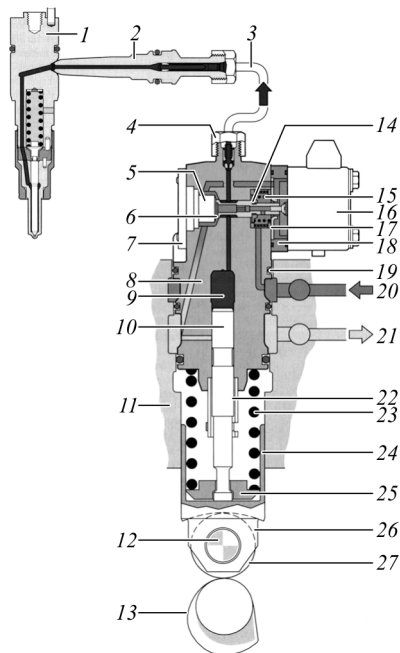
Схема системы насос – форсунка – трубопровод: 1 – форсунка; 2 – штуцер форсунки; 3 – трубопровод высокого давления; 4 – накидная гайка; 5 – упор; 6 – игла электромагнитного клапана; 7 – пластина; 8 – корпус насоса; 9 – полость высокого давления; 10 – плунжер; 11 – блок двигателя; 12 – ось роликового толкателя; 13 – кулачок; 14 – тарелка пружины; 15 – пружина электромагнитного клапана; 16 – корпус клапана с обмоткой электромагнита; 17 – пластина якоря; 18 – промежуточная пластина; 19 – уплотнение; 20 – вход топлива низкого давления; 21 – слив топлива; 22 – плунжер; 23 – пружина толкателя; 24 – тарелка толкателя; 25 – тарелка пружины; 26 – роликовый толкатель; 27 – ролик толкателя
